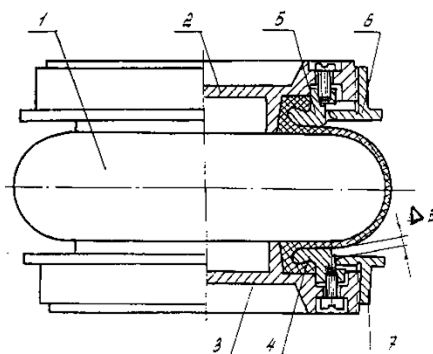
Устройство пневмоупругого баллона с буферным кольцом(а) (1 – резинокордная оболочка; 2,3 – фланцы; 4,5 – крепежные кольца; 6, 7 – буферные кольца, Δ_z – зазор.
